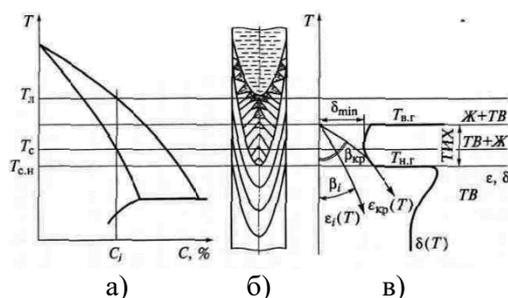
Схема процесса образования горячих трещин в сварных швах
